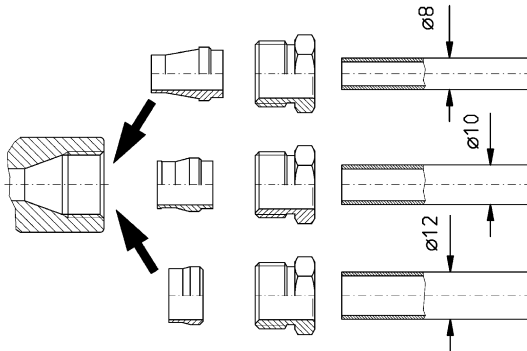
Kit de raccordement universel Afriso-Eurojauge
